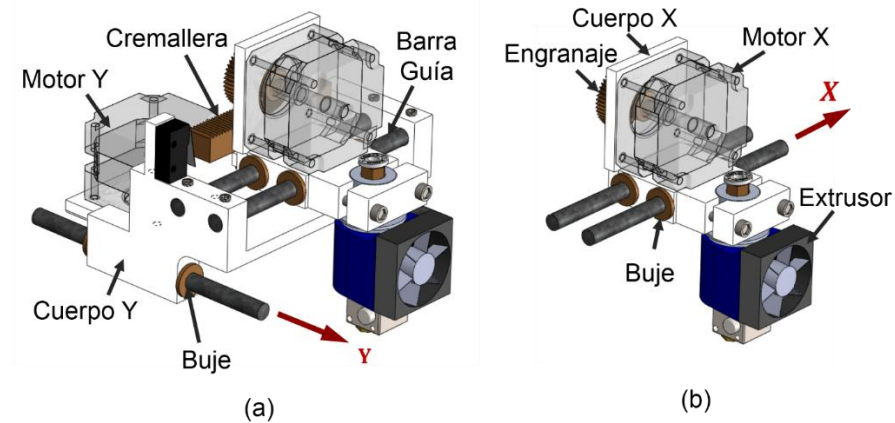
Partes que debe trasladar cada motor del sistema motriz de la parte impresora (a) el motor adjunto al cuerpo móvil Y debe movilizar el extrusor, 8 bujes, 2 engranajes, cuerpo móvil X e Y, 2 barras de acero, una cremallera y su propia masa (b) el motor adjunto al cuerpo móvil X debe desplazar el extrusor, 4 bujes, un engranaje, el cuerpo móvil X y su propio peso.
